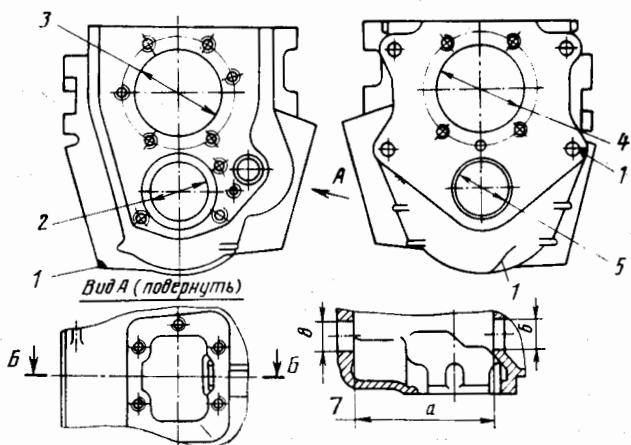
Основные дефекты картера коробки передач автомобиля ЗИЛ-431410
